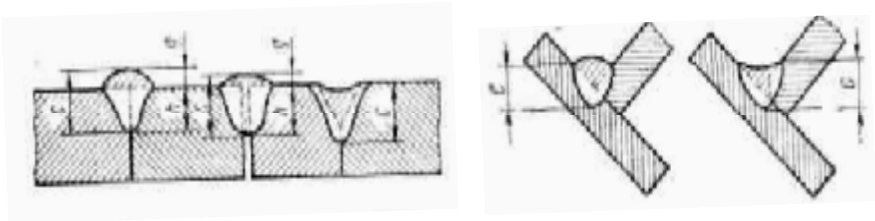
Вплив обробки кромки і величини зазору на форму шва й частку основного металу в ньому
